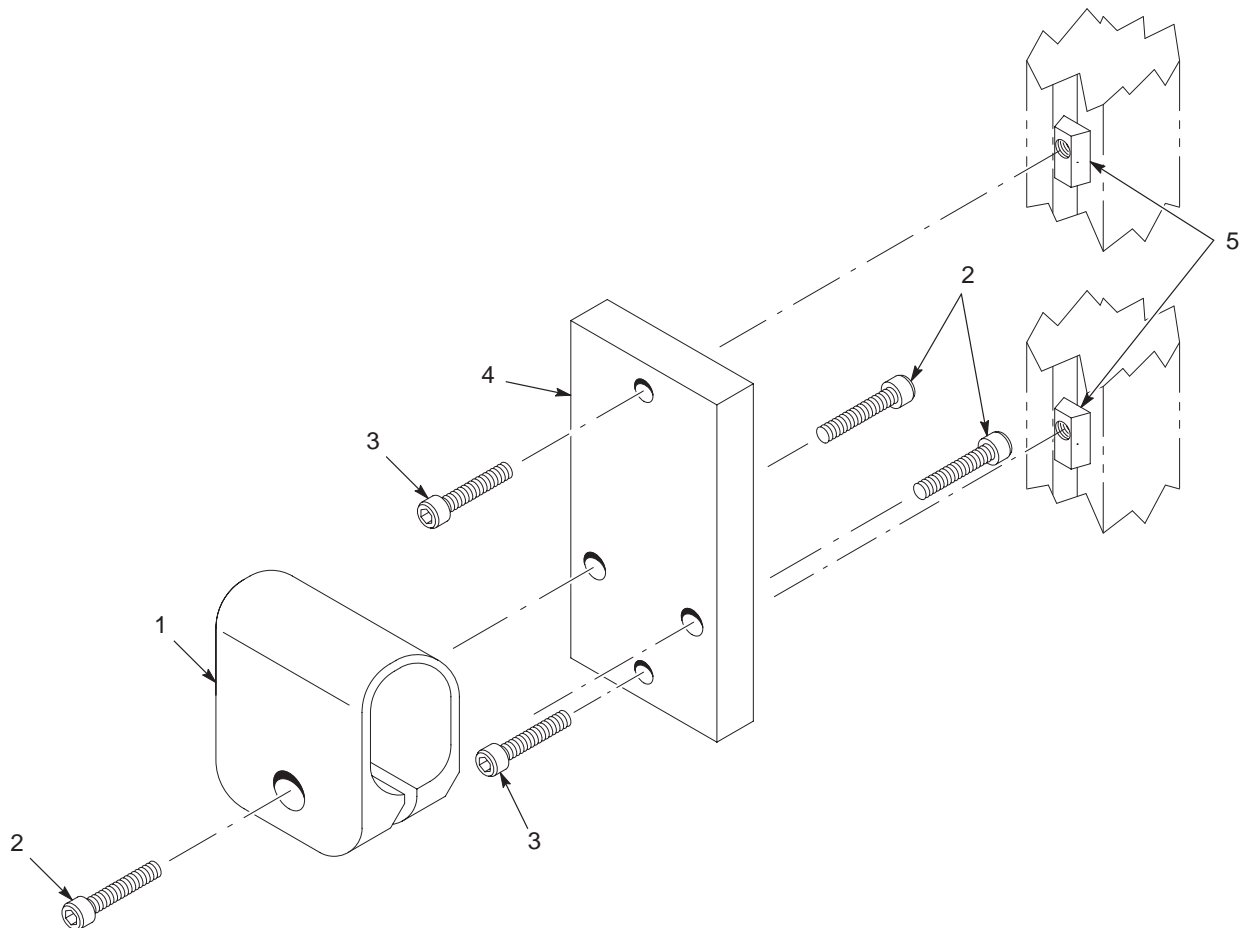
Drejemontering på holdestang af pistoler til rørmontering
